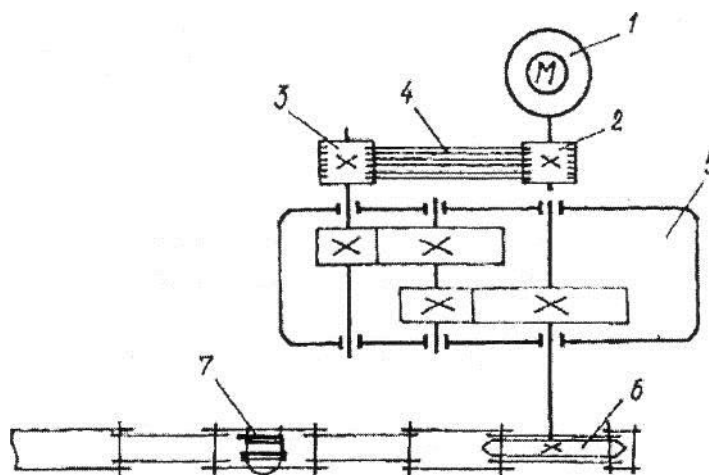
Навозоуборочный конвейер кругового движения типа ТСН-160А
